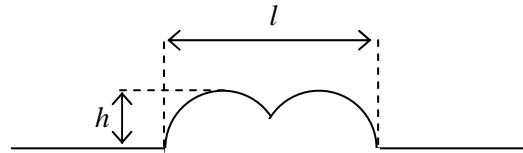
Définitions de la largeur caractéristique des cordons de soudure (l)
